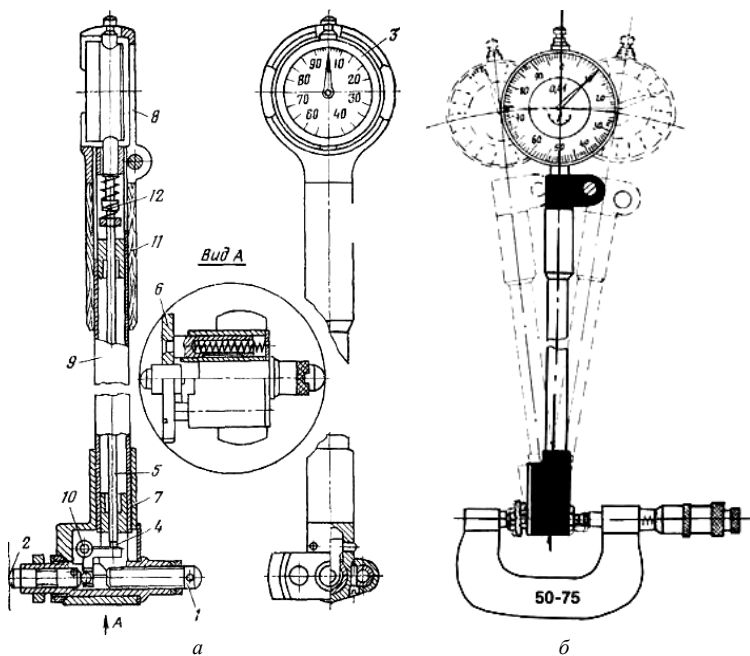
Индикаторный нутромер с рычажной передачей: а – схема индикаторного нутромера; б – установка индикаторного нутромера на нуль; 1 – подвижный (измерительный) стержень; 2 – неподвижный (регулируемый) стержень; 3 – индикатор часового типа; 4 – двуплечий рычаг; 5 – шток; 6 – центрирующий мостик; 7 – корпус; 8 – кожух; 9 – трубка; 10 – ось вращения рычага; 11 – теплоизоляционная втулка (рукоятка); 12 – пружина
